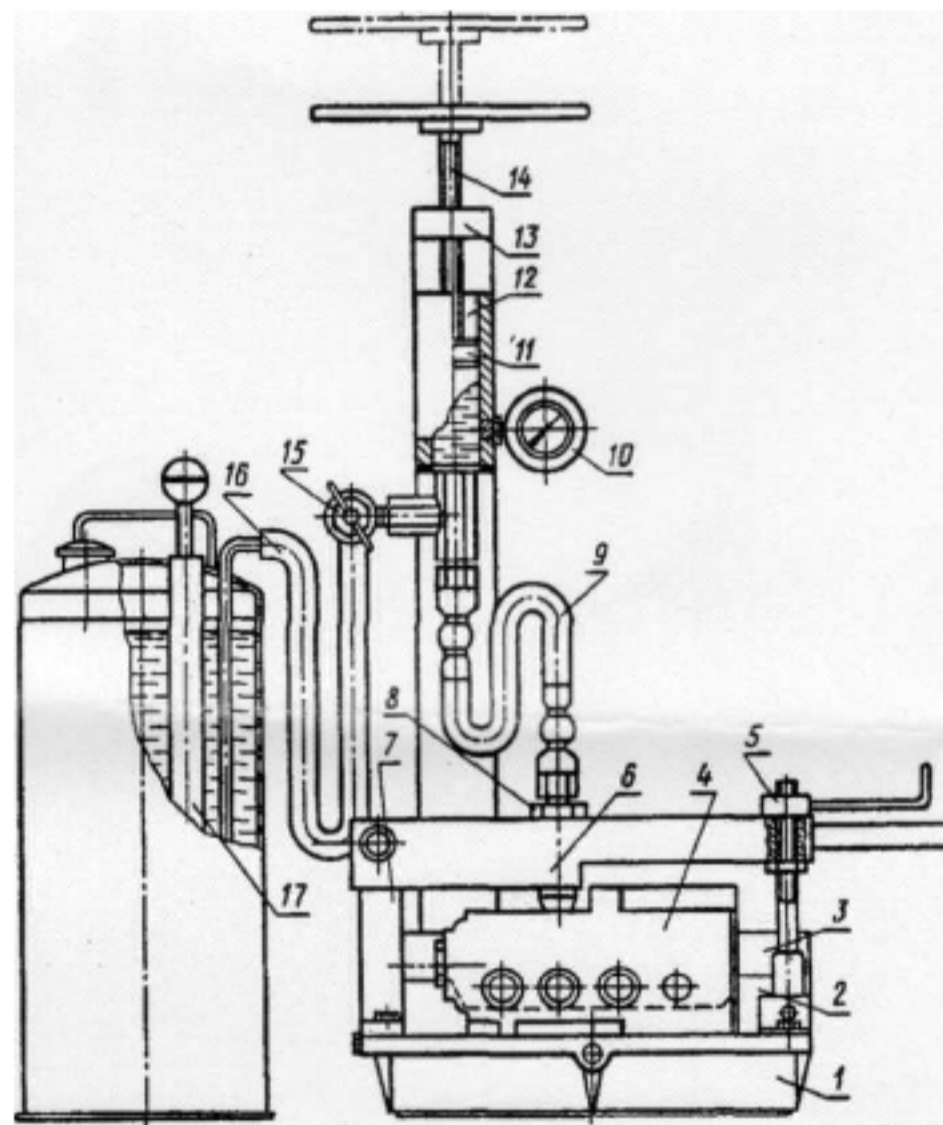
Прилад для контролю гідравлічної щільності золотникових пар: 1 - плита; 2 і 3 - упорні пластини; 4 - корпус розподільника із золотниками; 5 - гвинт затискача; 6 - затискач; 7 - стійка затискача; 8 - конусний штуцер; 9 - шланг високого тиску; 10 - манометр; 11 - поршень; 12 - циліндр; 13 - стійка; 14 - гвинтова пара; 15 - вентиль; 16 – сполучний шланг; 17 - нагнітач масла
